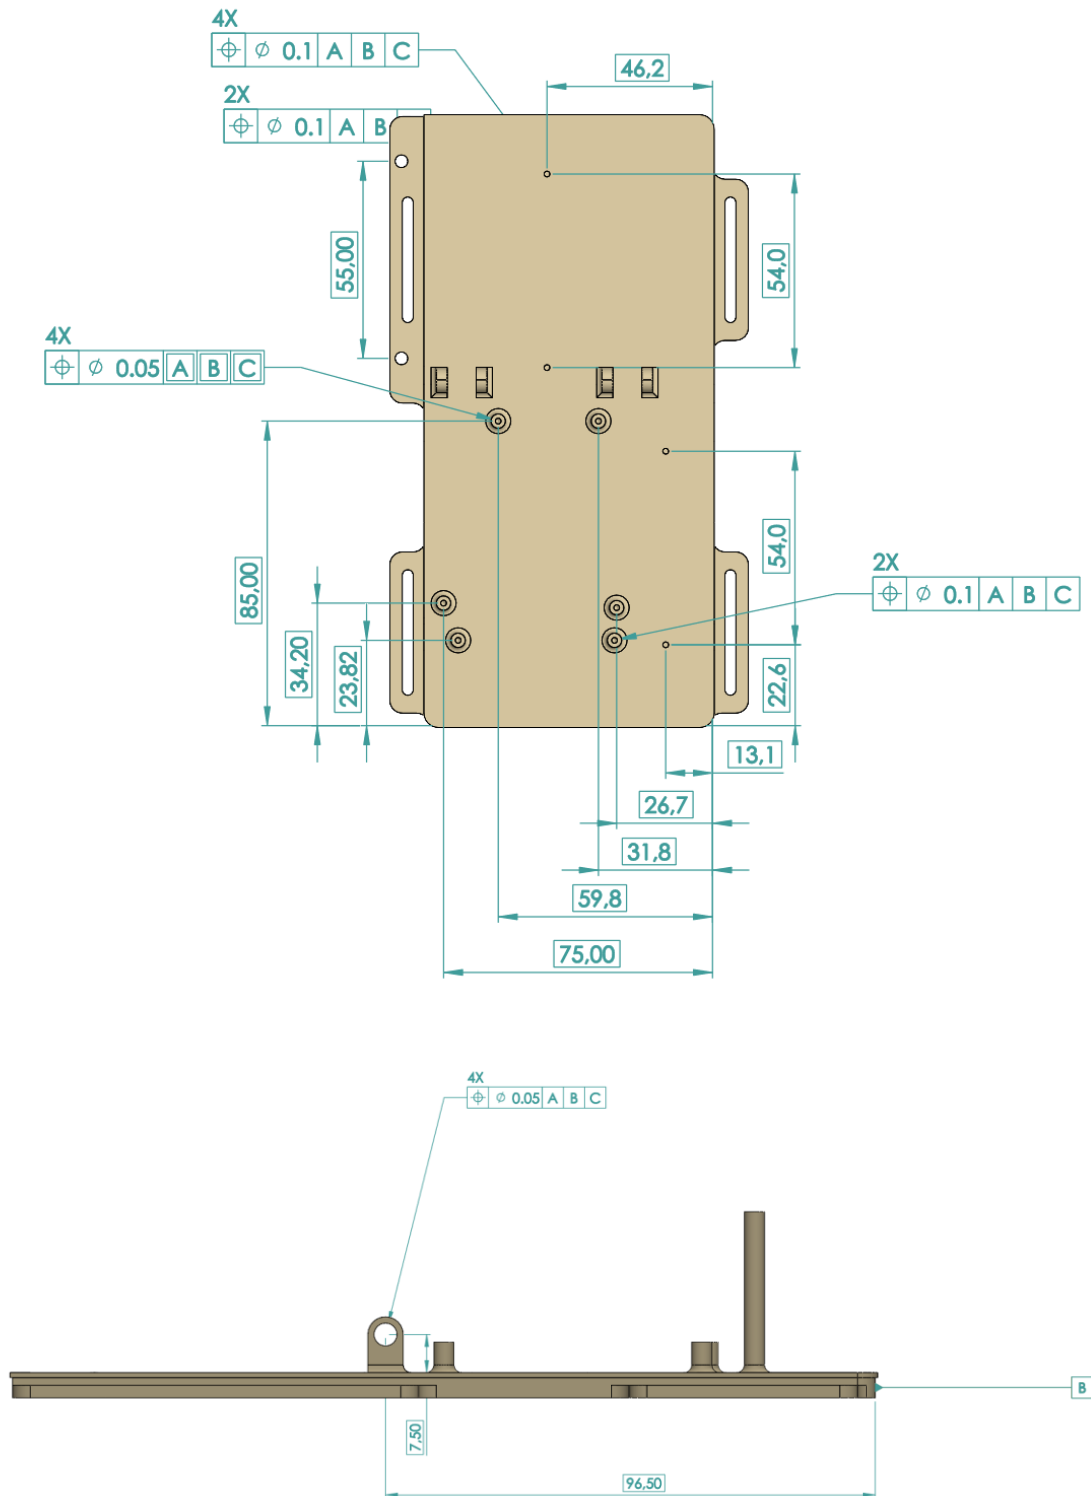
Tolerancias geométricas "Apoyo antebrazo"
